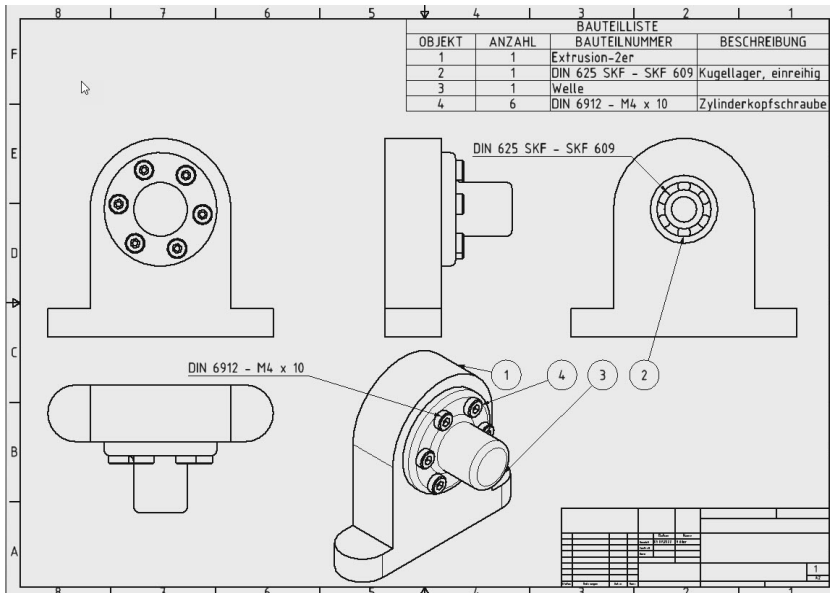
Zeichnung für eine Baugruppe mit Stückliste und Positionsnummern
